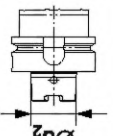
Полый конический хвостовик типа U с резьбой для устройства подачи смазочно-охлаждающей жидкости
